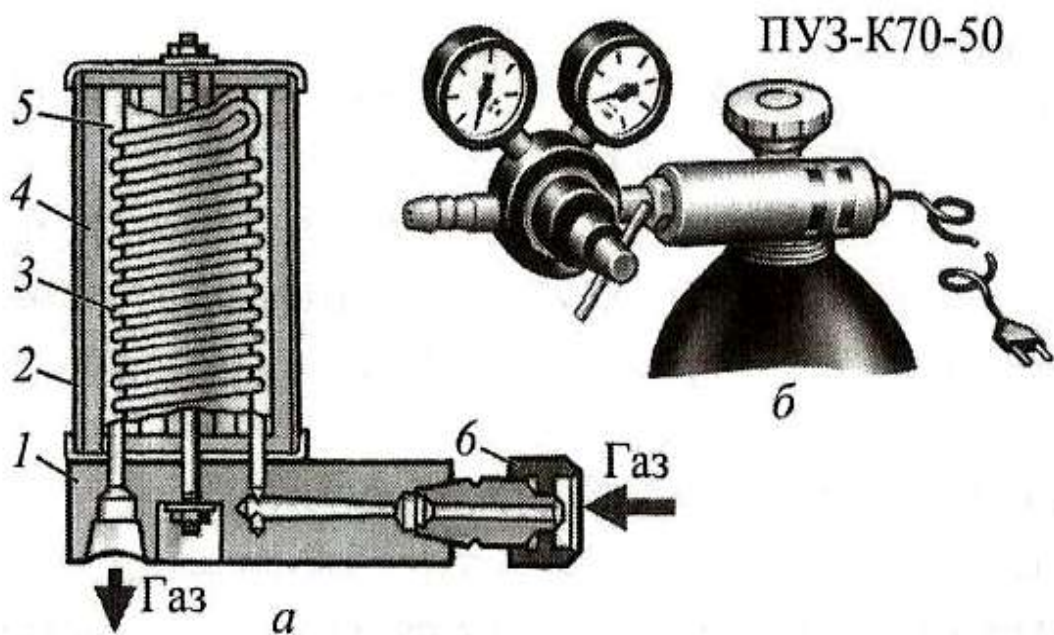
Устройство (а) и общий вид (б) подогревателя:
